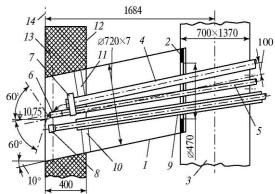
Пылемазутная прямоточная горелка котла ТП-87: I — корпус; 2 — ограничительная шайба; 3 — воздушный короб; 4 — труба ПВК \oslash 89х6 мм; 5 — труба сжатого воздуха \oslash 42х5 мм; 6 — струйный распыливающий насадок; 7 — хомут; 8 — головка паромеханической форсунки; 9 — форсуночная труба; 10 — пластины крепления форсуночной трубы; 11 — пластины крепления трубы ПВК; 12 — короб амбра зуры (приваривается через накладки к экранным трубам); 13 — экранные трубы, разведенные внутрь амбразуры; 14 — ось экранных труб
